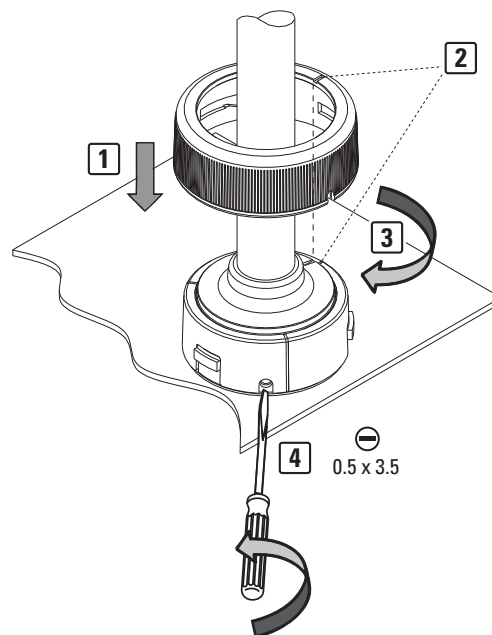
Befestigen des Basismoduls auf dem Schnellmontageadapter
